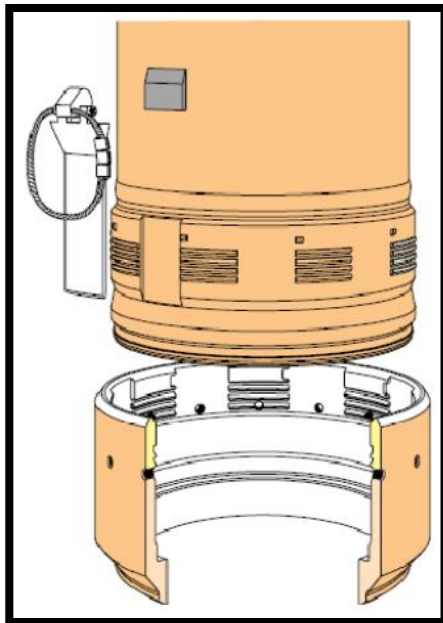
Ensamble de conector Quick jay, drill quip, 2015
